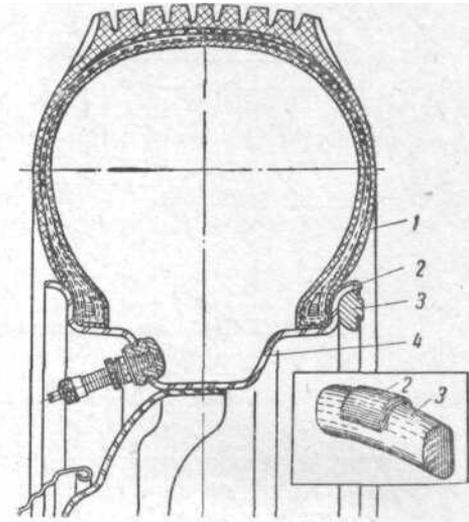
Крепление балансирующего грузика на ободе колеса:
